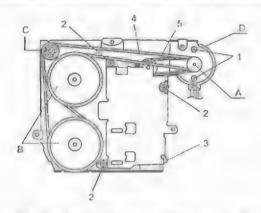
1 — крепление электродаизателя; 2 — крепление механизма шестерен; 3 — направляющая; 4 — пассик; 5 — короткий пассик (в зависимости от типа конструкции ЛПМ); А — шкиф электродвизателя; В — механизм ведущего вала; С — средний шкив; D — электродвизатель
